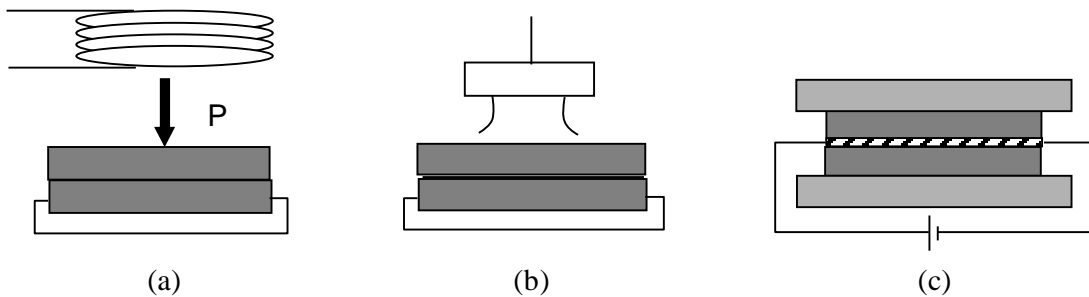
2 : Représentation schématique : (a) du soudage par induction, (b) du soudage par résistance, (c) du soudage par résistance
